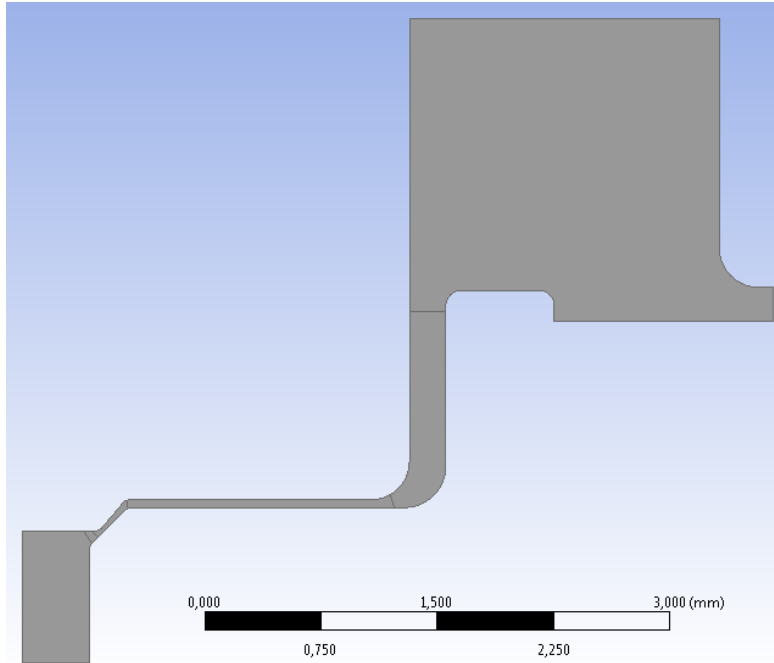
Geometria con poppet a spina cilindrica con spalla. L'altezza del canale orizzontale è pari a 0.1 mm.
